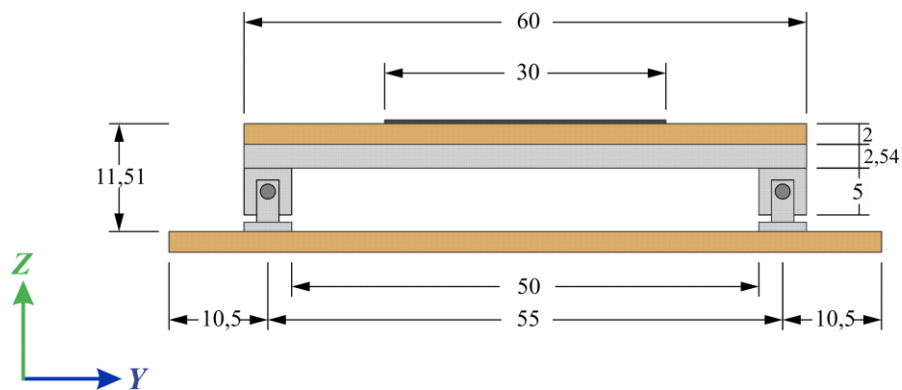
Seção transversal da mesa vibratória – Corte B-B. Dimensões em centímetros.
